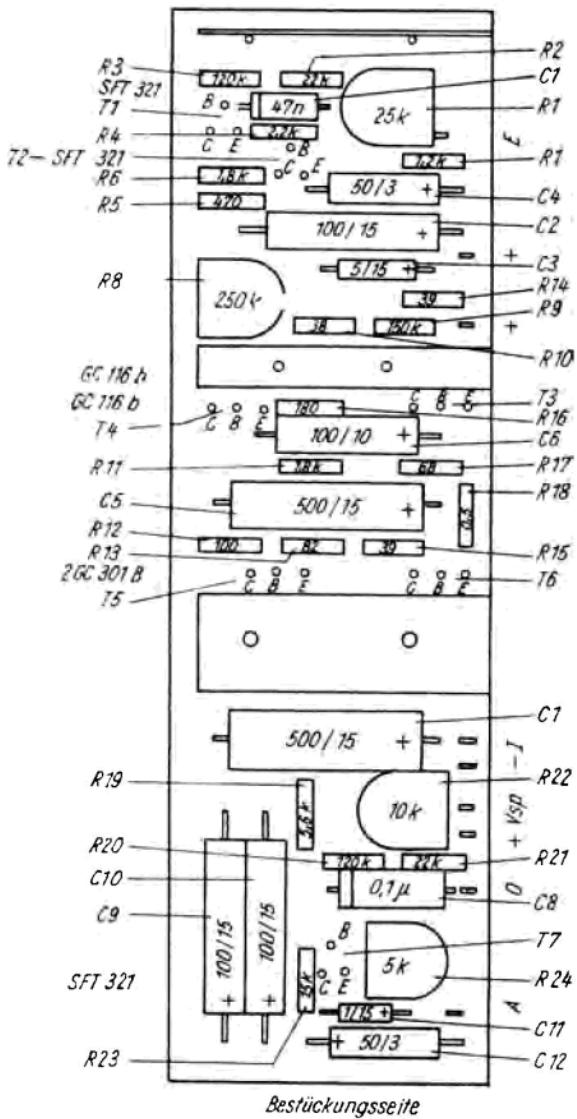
Bestückungsplan zum Hallverstärker nach Stromlaufplan
